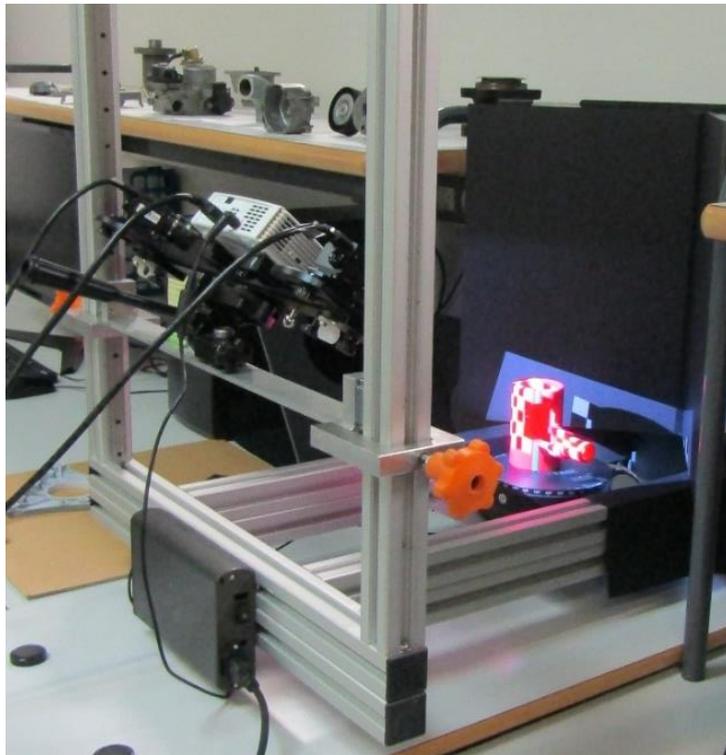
Colocación de pieza y fondo negro tras la calibración.
